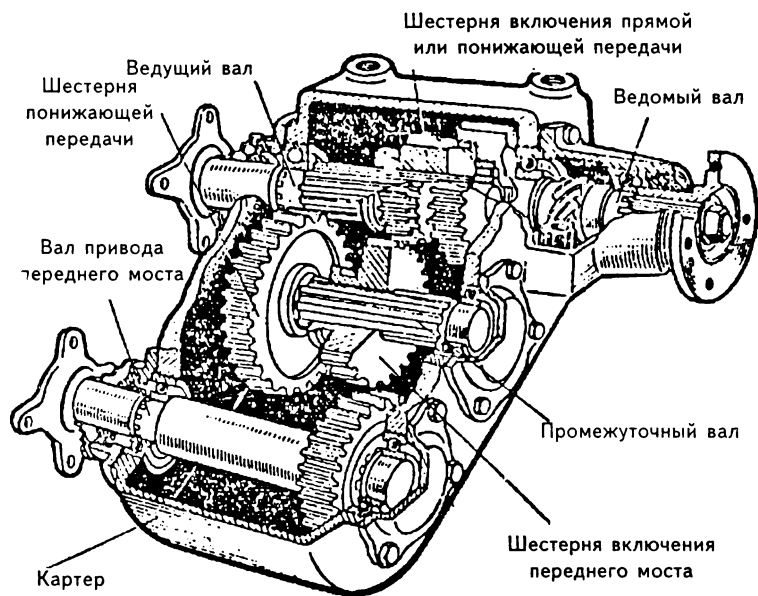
Раздаточная коробка автомобиля ГАЗ-66
